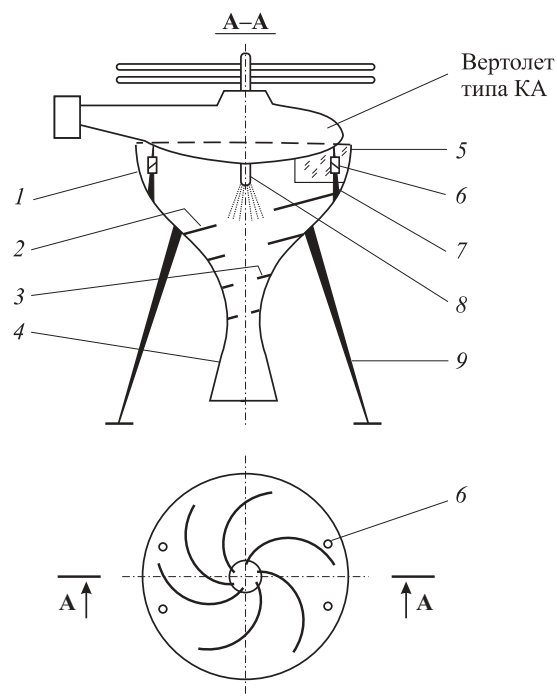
Схема устройства “Смерч” для тушения пожаров [25]: 1 — верхняя собирающая круглая стенка корпуса; 2 — спираль для закручивания воздуха; 3 — спираль для закручивания воздуха в сужающейся части корпуса; 4 — сопло Лавала; 5 — прозрачная часть стенки корпуса для обзора местности; 6 — автосцепка; 7 — стойка с нижней частью автосцепки; 8 — поддерживающие корпус стойки
